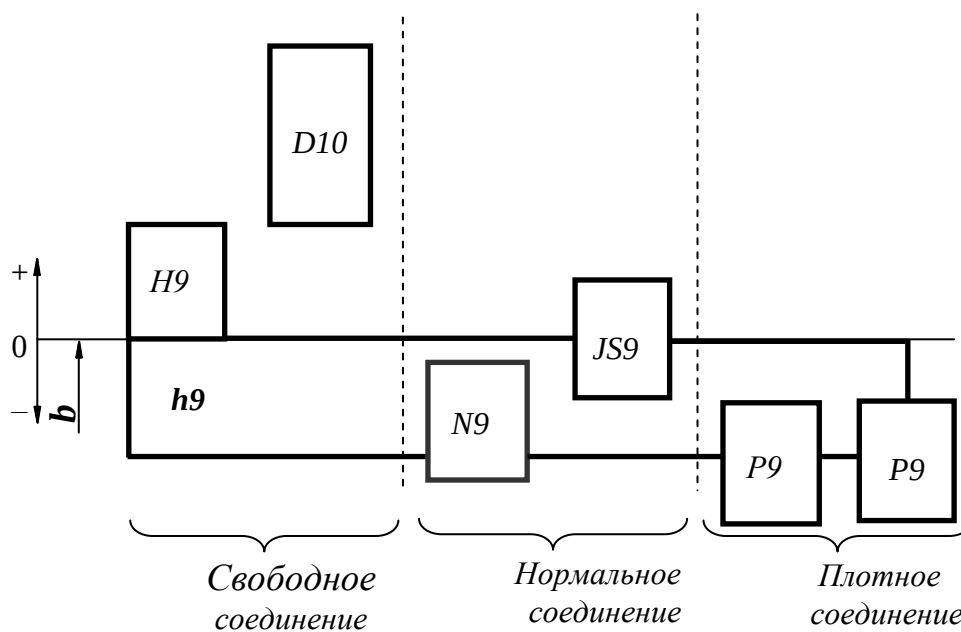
Схемы полей допусков шпоночных соединений с призматическими шпонками: H9, N9, P9 – поля допусков ширины паза вала; D10, JS9, P9 – поля допусков ширины паза втулки; h9 – поле допуска ширины шпонки
